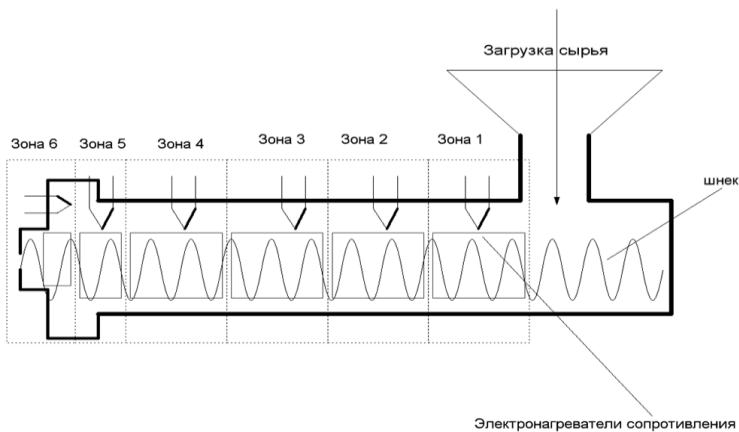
Общий вид экструдера с установленными датчиками и нагревателями сопротивления
